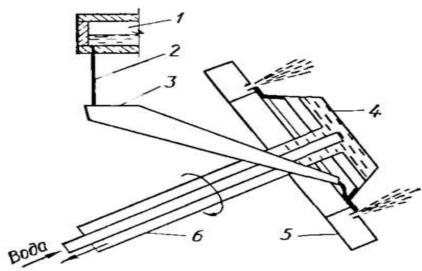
Схема центробежно-дутьевой установки, где 1– вагранка; 2 – струя расплава; 3–направляющий желоб; 4– раздаточная чаша; 5 – дутьевое кольцо; 6 – приводной вал.
